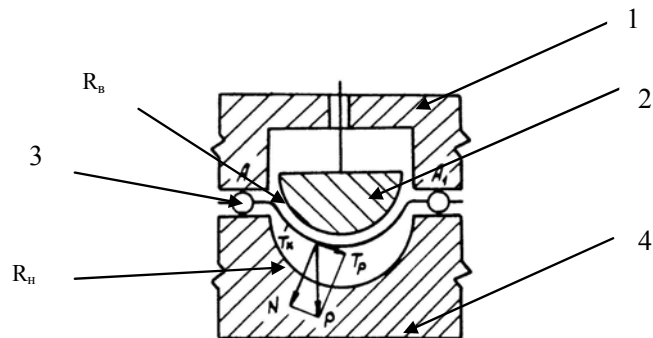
Конструкція елементів подушок преса для об'ємного формування деталей одягу: 1 – верхня подушка; 2 – пуансон; 3 – тканина; 4 – нижня подушка
